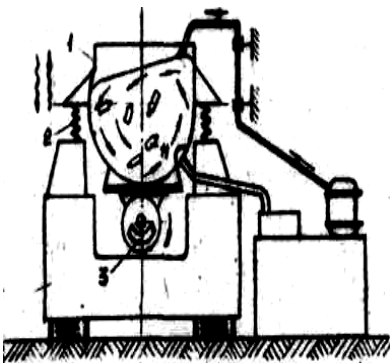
Схема вибрационной установки: 1-рабочая камера; 2-пружина; 3-вал с несбалансированными грузами; 4-станина
